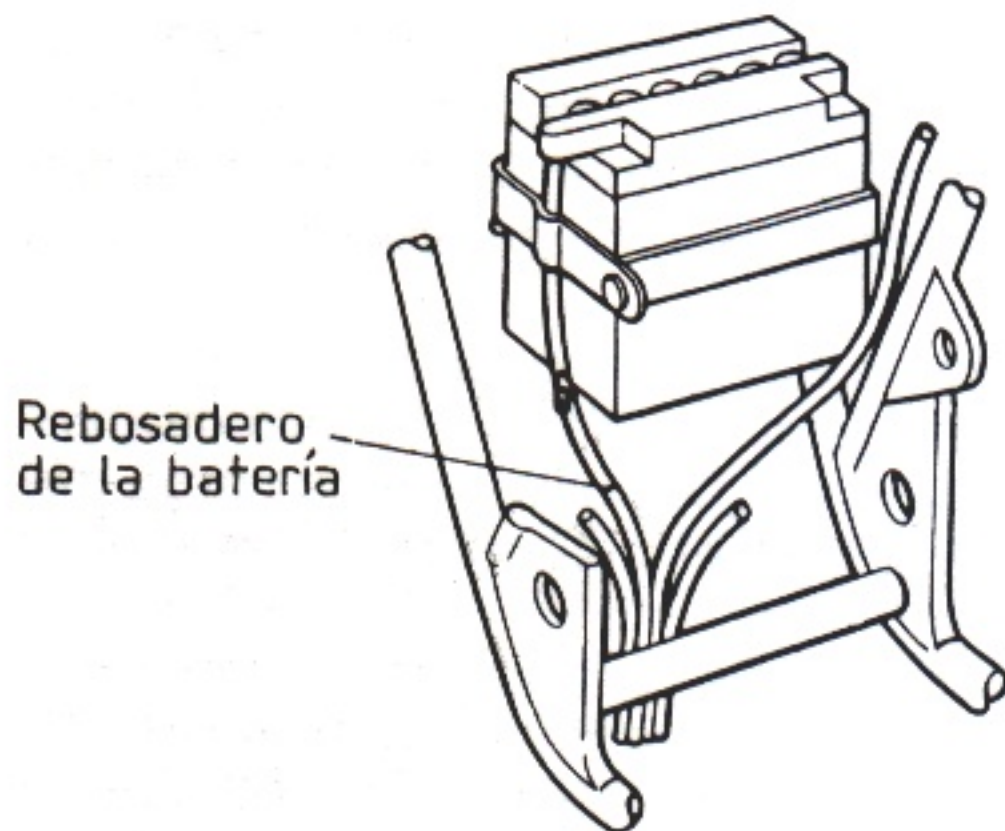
Situación del ^{tubo} rebosadero de la batería.
